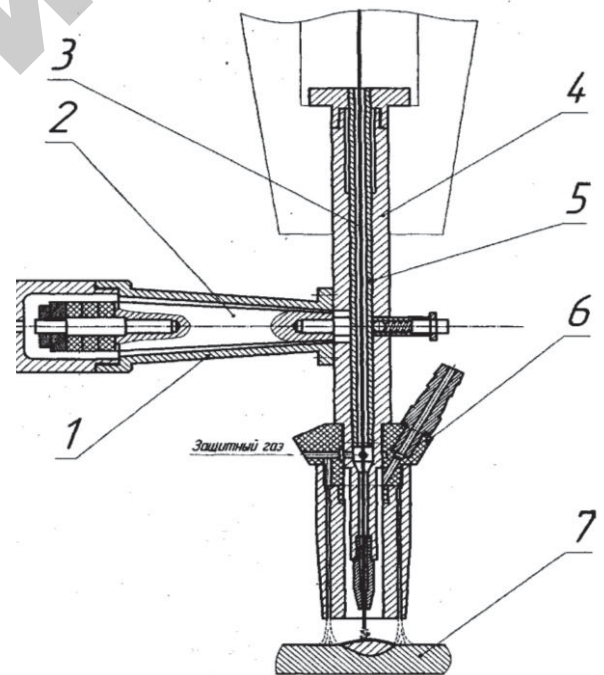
Схема технологической оснастки для введения ультразвуковых колебаний и порошкового материала в зону наплавки: 1 – устройство передачи УЗК на электрод; 2 – волновод-концентратор; 3 – электродная проволока; 4 – корпус наплавочной головки; 5 – токовод; 6 – устройство для подачи газопорошковой смеси; 7 – наплаваемая поверхность
